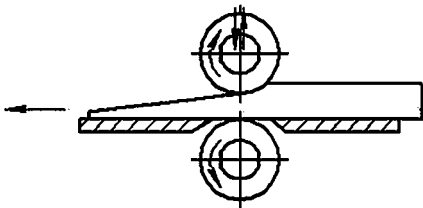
Схема прокатки в цилиндрических валках с изменением межвалкового зазора
